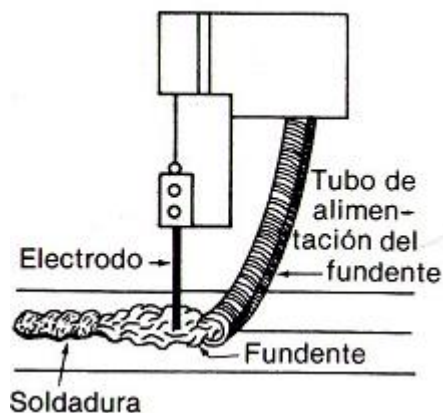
Proceso de soldadura de arco sumergido.
